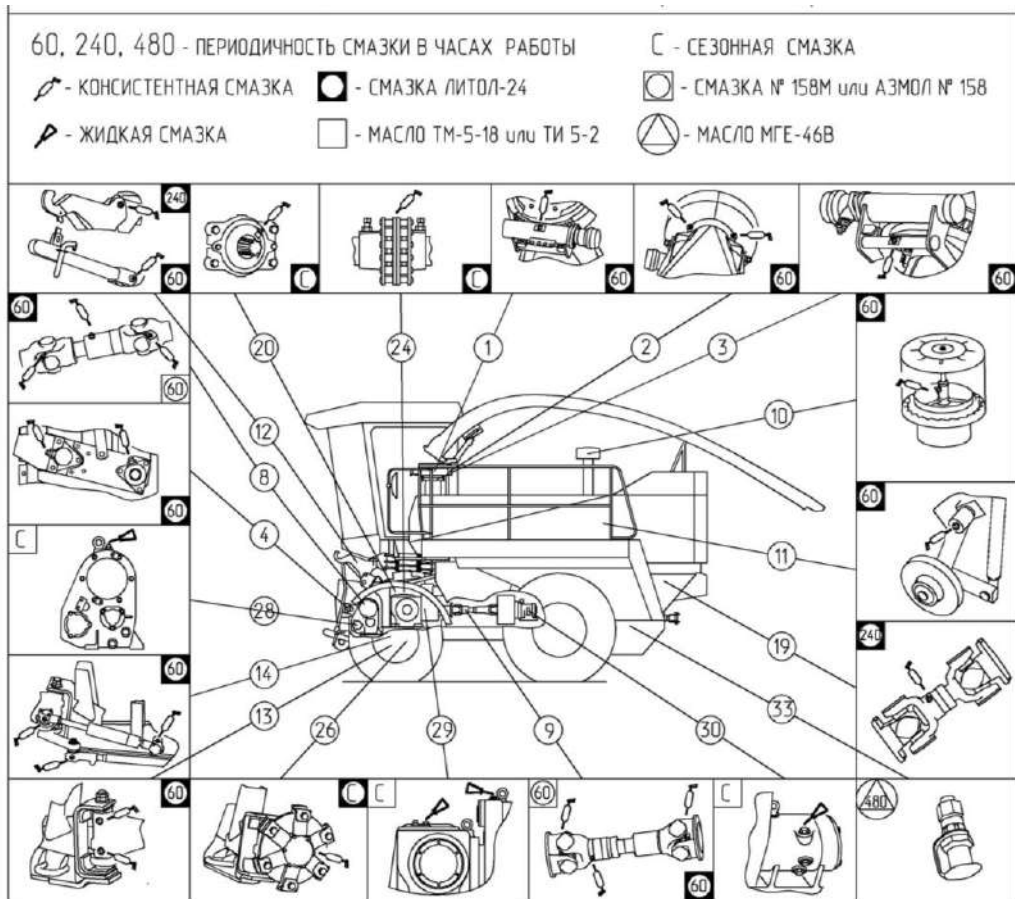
Схема смазки комбайна (вид слева)
